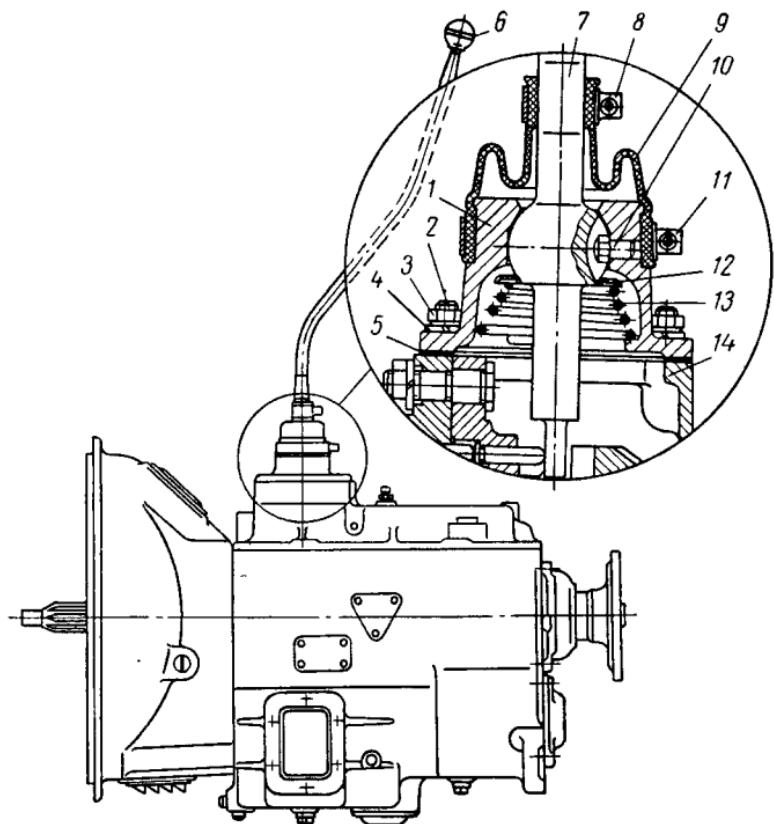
Коробка передач ЯМЗ-236С и рычаг переключения передач:
